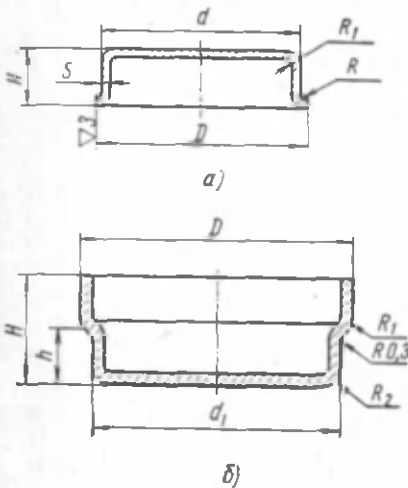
Контрольные размеры крышки и корпуса пуговичного ртутно-цинкового элемента:
